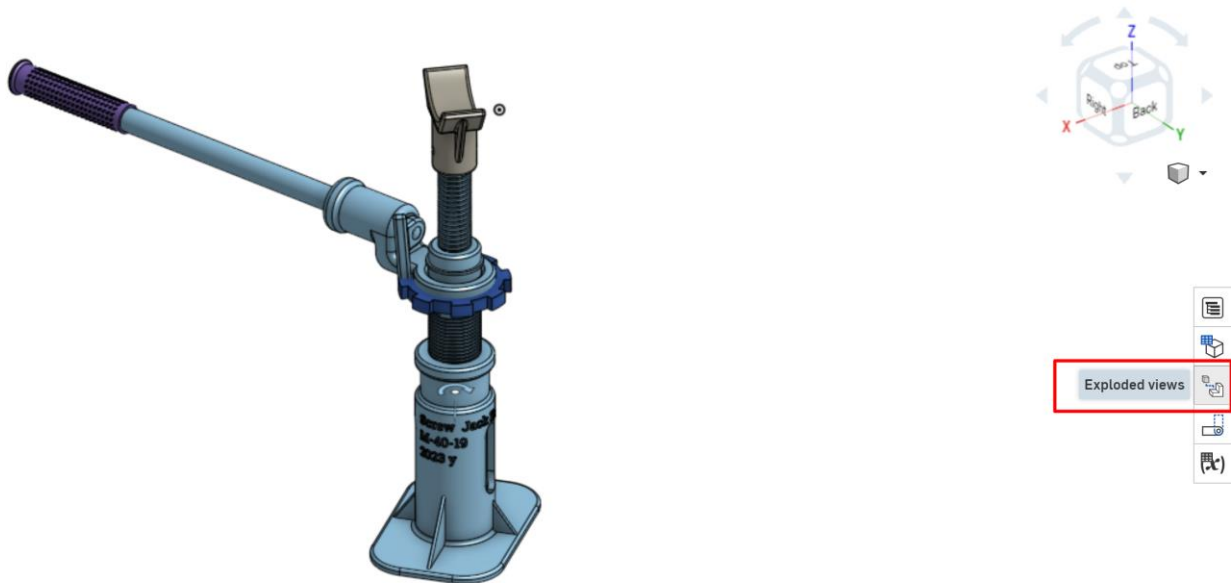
Створення вибухового креслення за допомогою Exploded view
